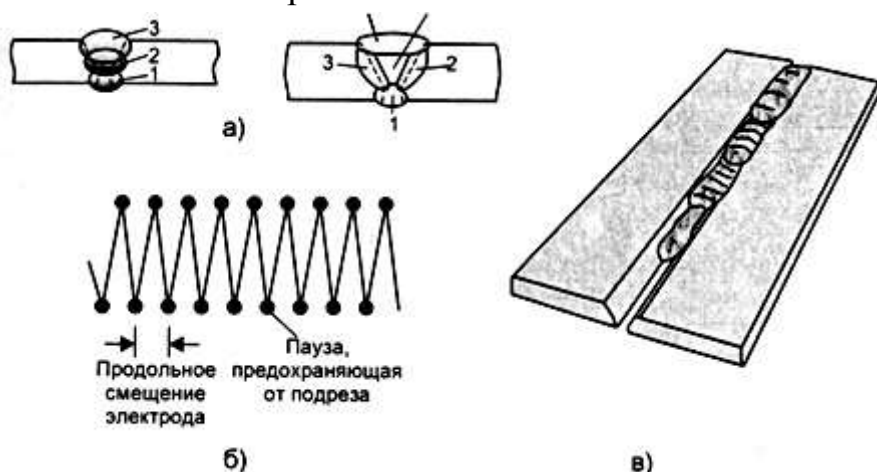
Сварка стыкового соединения со скосом кромок в нижнем положении.
